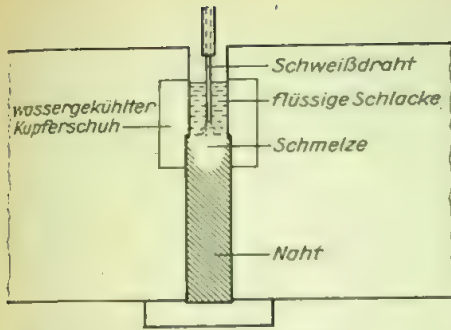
Elektro-Schlacke-(ES)-Schweißen
